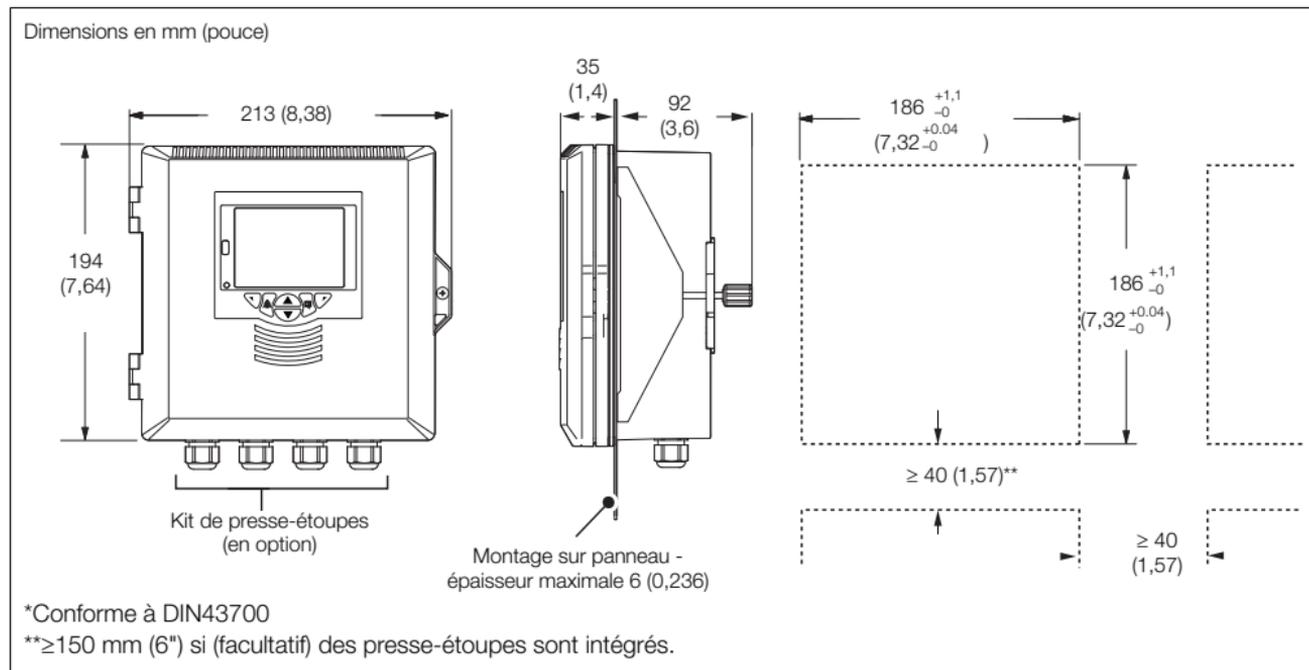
Option de montage sur panneau du ControlMaster CMF160
